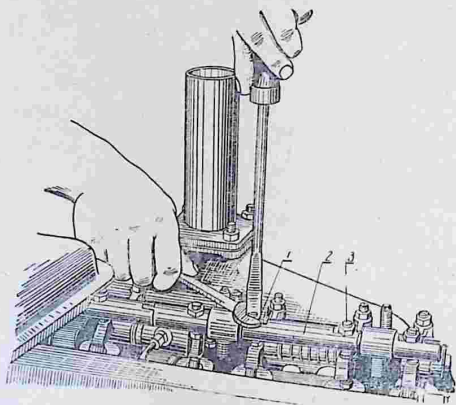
Регулировка декомпрессионного механизма двигателя Д-40К:
